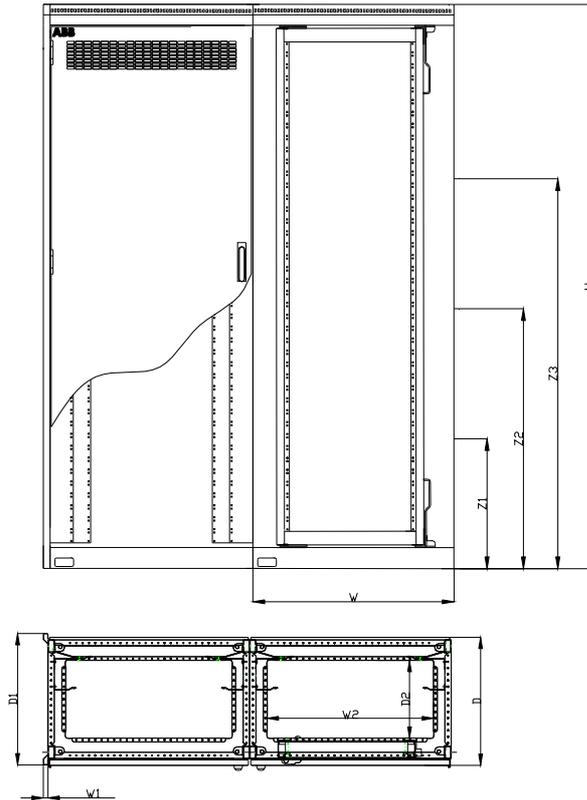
Montaje conjunto de los armarios – Posición de los tornillos
